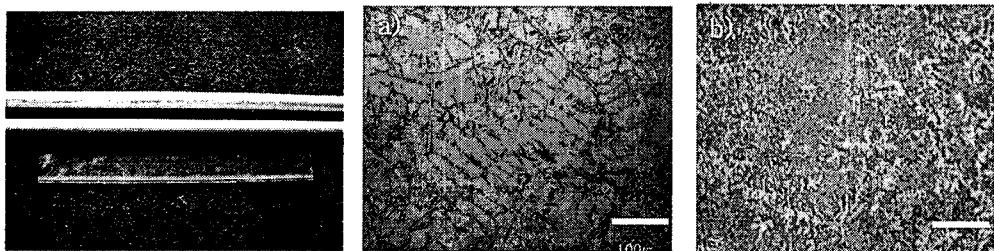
재활용 전신재용의 압출재 및 미세조직 사진 (a) Die casting 재 (b)전신재
